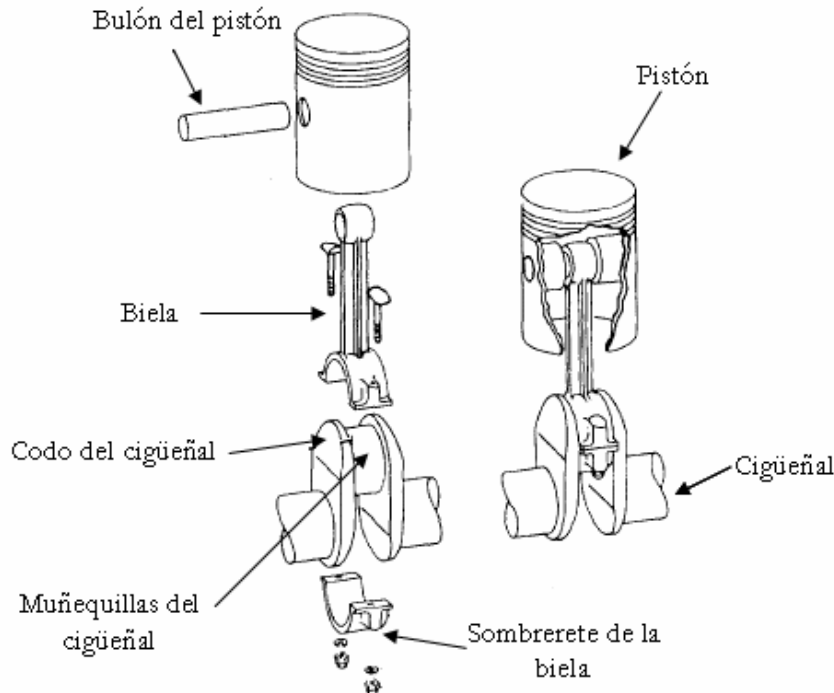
Componentes del sistema mecánico interno principal del motor
